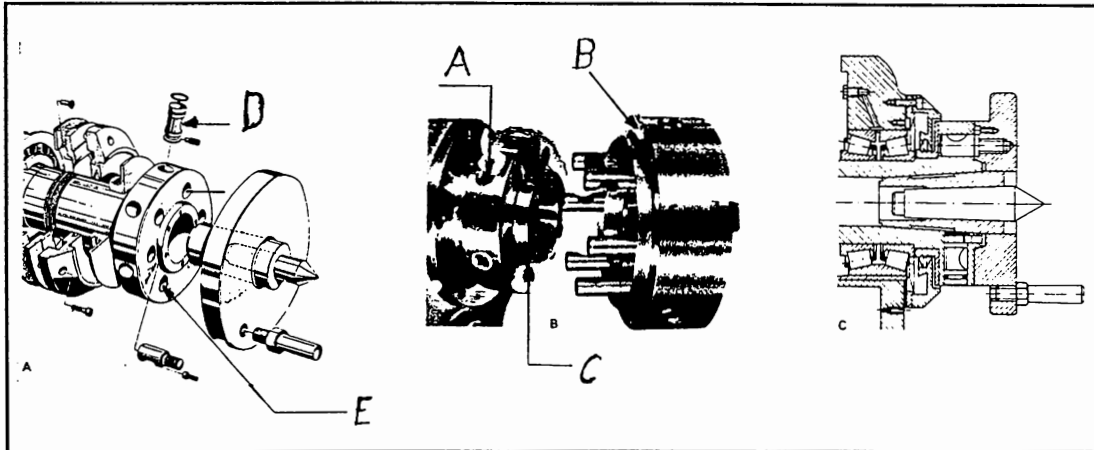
Sistema Camlock: A, despiece; B, forma de acoplamiento; C, conjunto.
